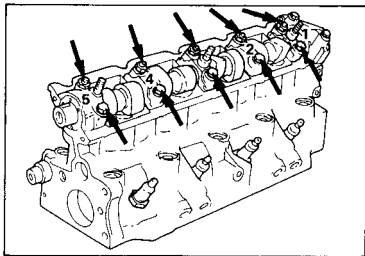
Пронумеруйте крышки подшипников распределительного вала
